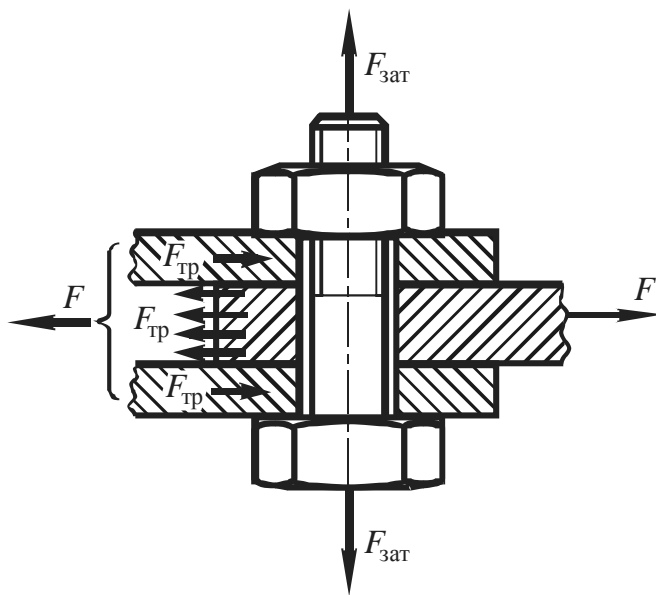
Схема болтового соединения установленного в отверстие деталей с зазором
